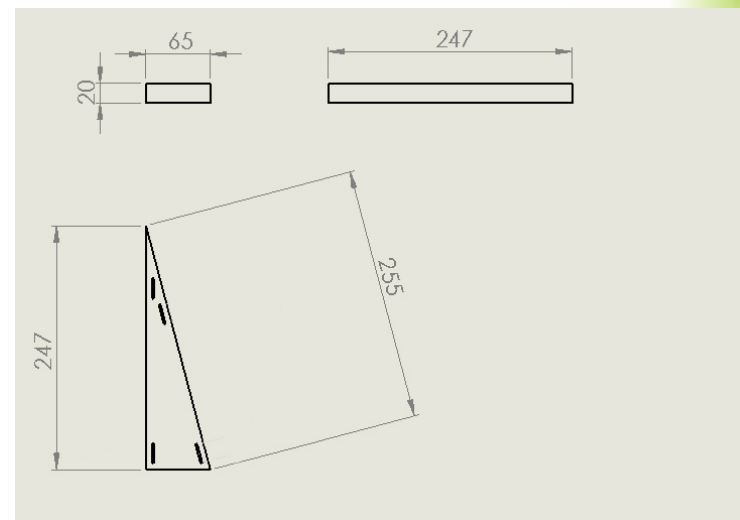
Desenho técnico da peça triangular de 247 x 65 x 20 mm
